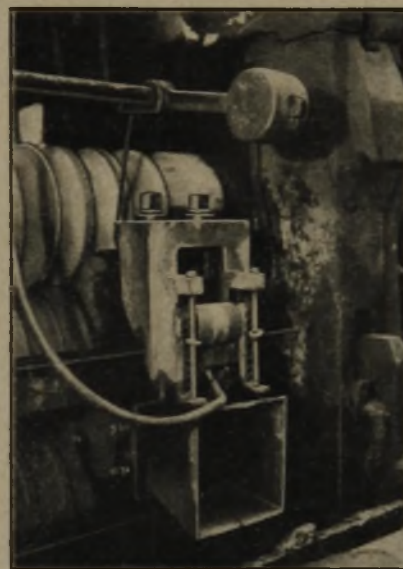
Ausführung mit Rolle an einer Ovalwalze.
